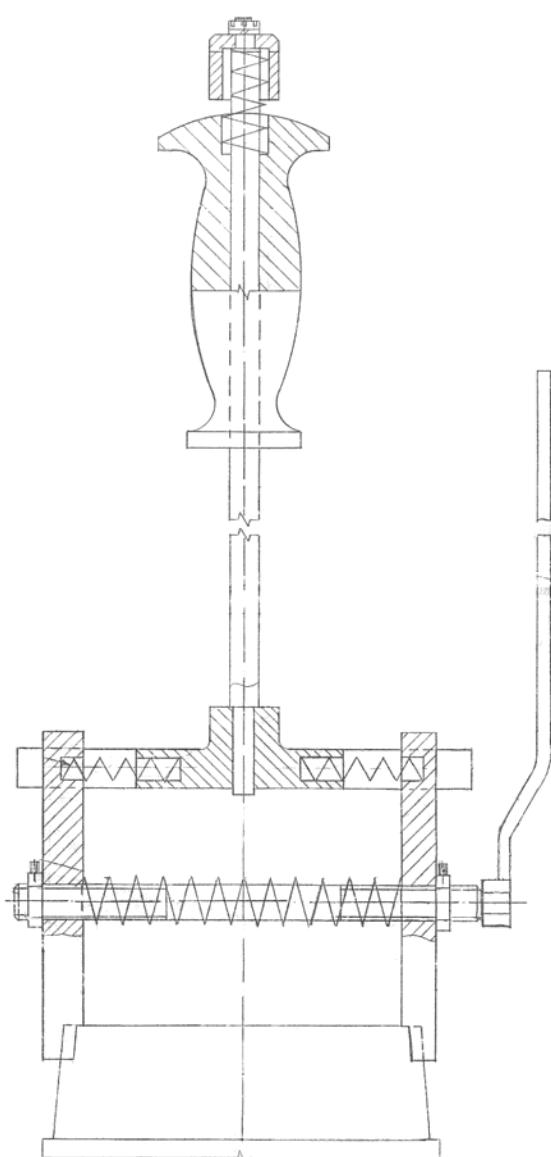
ЗМ 7814-5146, Съемник для снятия крышек коренных подшипников
